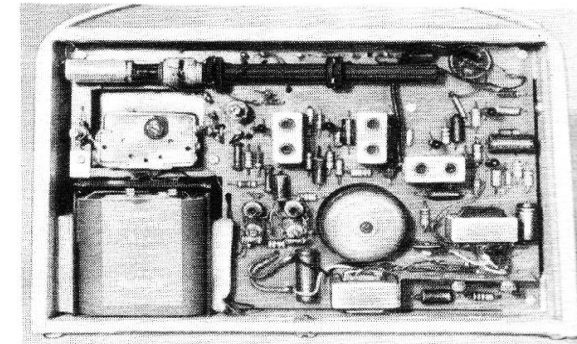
Innenansicht des Gerätes von der Bestückungsseite
